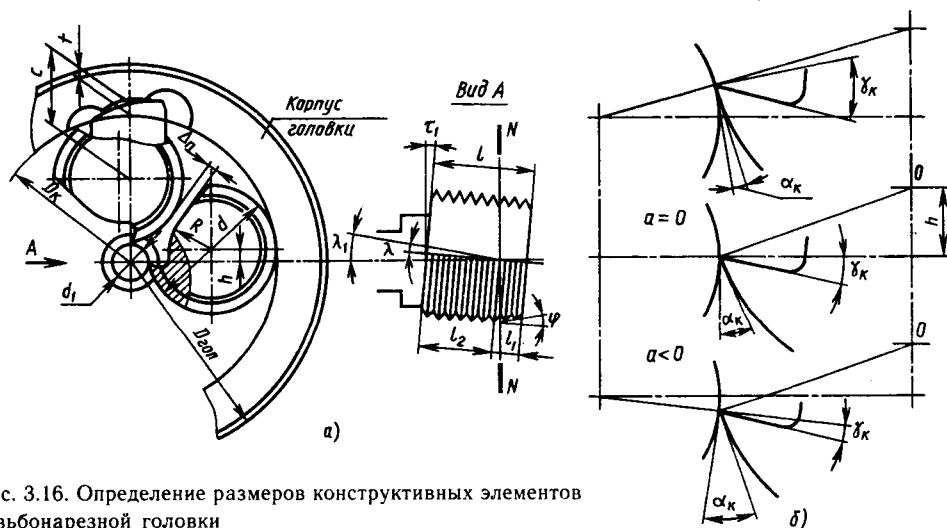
Определение размеров конструктивных элементов резьбонарезной головки
